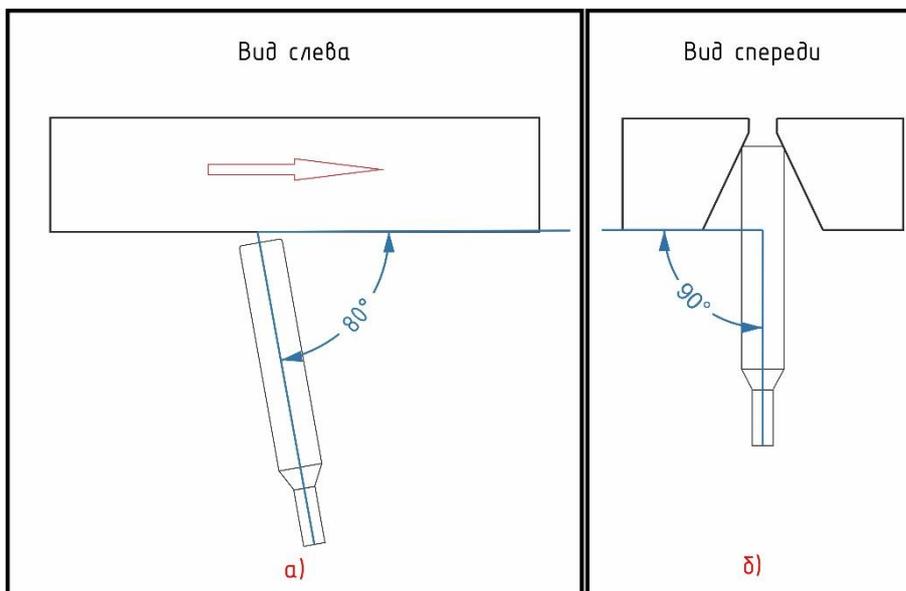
Положение электрода при сварке корневых проходов
